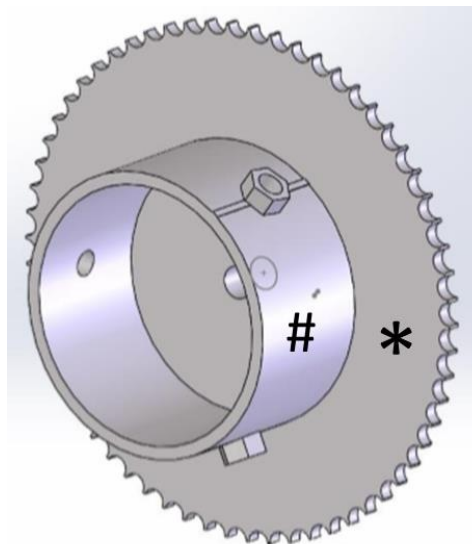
Roda dentada (Engrenagem) (\*) com Tubo de Fixação (#).
